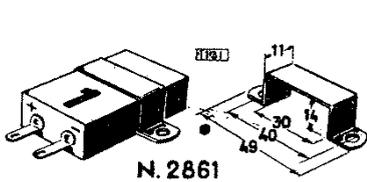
Fascetta per il montaggio orizzontale di un elettrolitico del tipo 1
